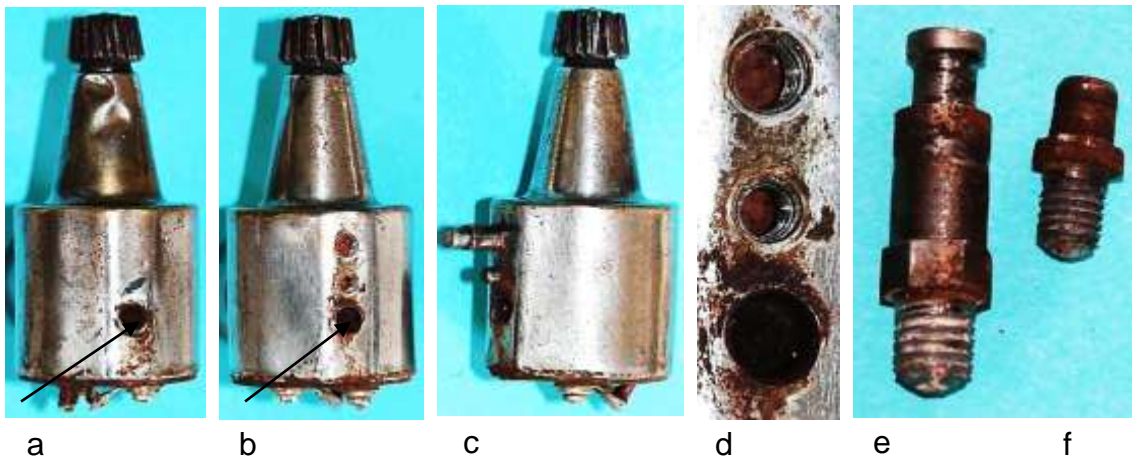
Bohrungen des Dynamokörpers: a) Bohrloch für den Drehzapfen des Basisblechs, b) Bohrloch für den Drehzapfen des Winkelblechs, c) Winkelblechseite mit Federzapfen und Sperrstift, d) Zwei Gewindelöcher und ein Grundloch auf der Winkelblechseite, e) Federzapfen, f) Sperrstift
